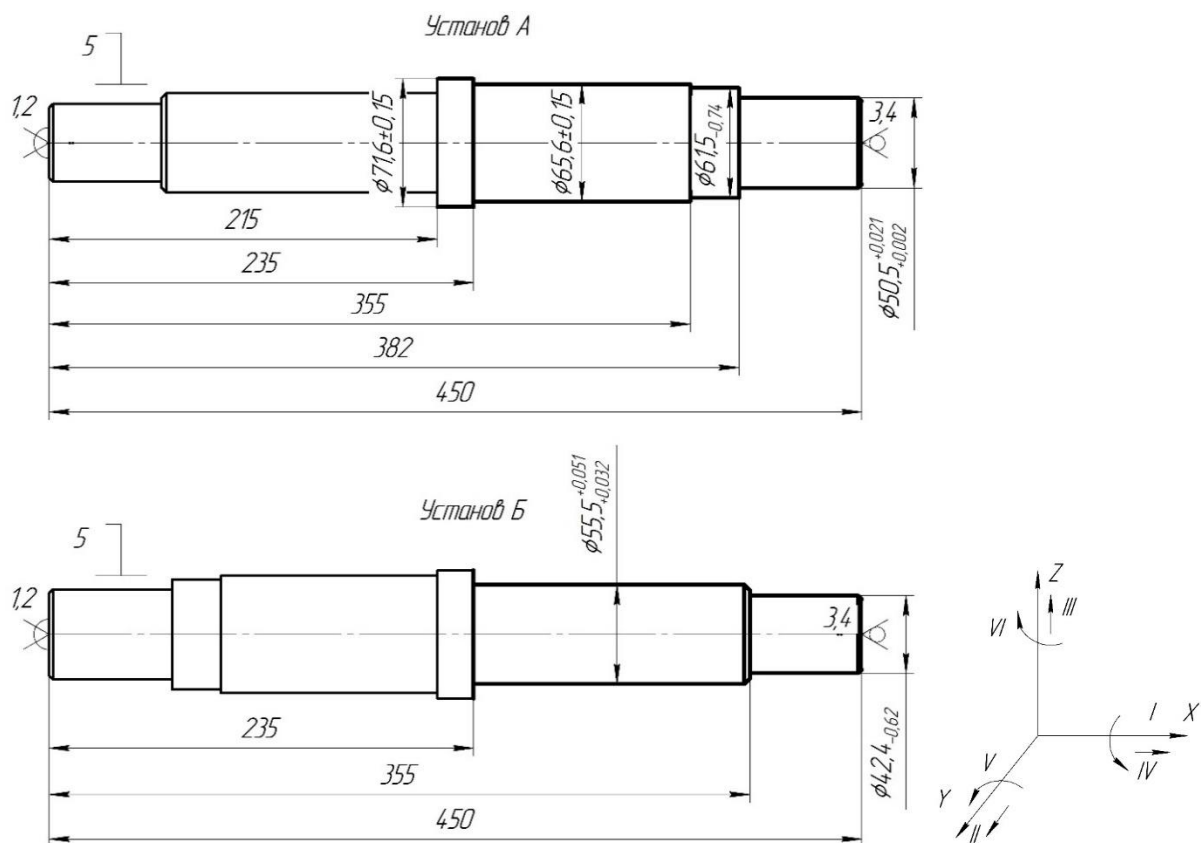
Схема базування заготовки в повідковому патроні
